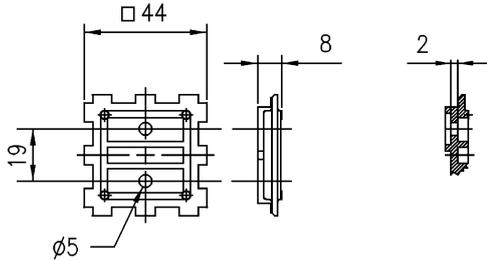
Draufsicht und Querschnitt von der Adapterplatte
